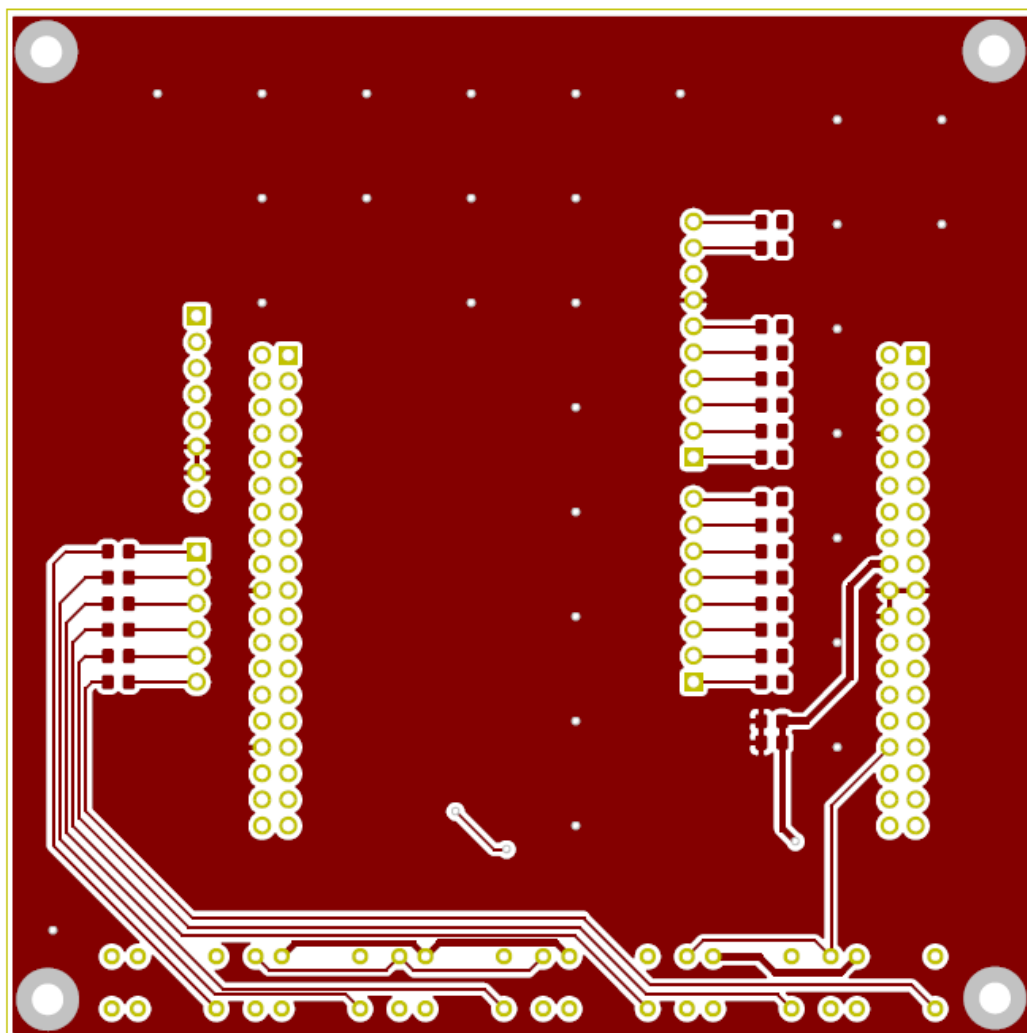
Schemat layoutu PCB łóżka testowego dla wariantu 1.
